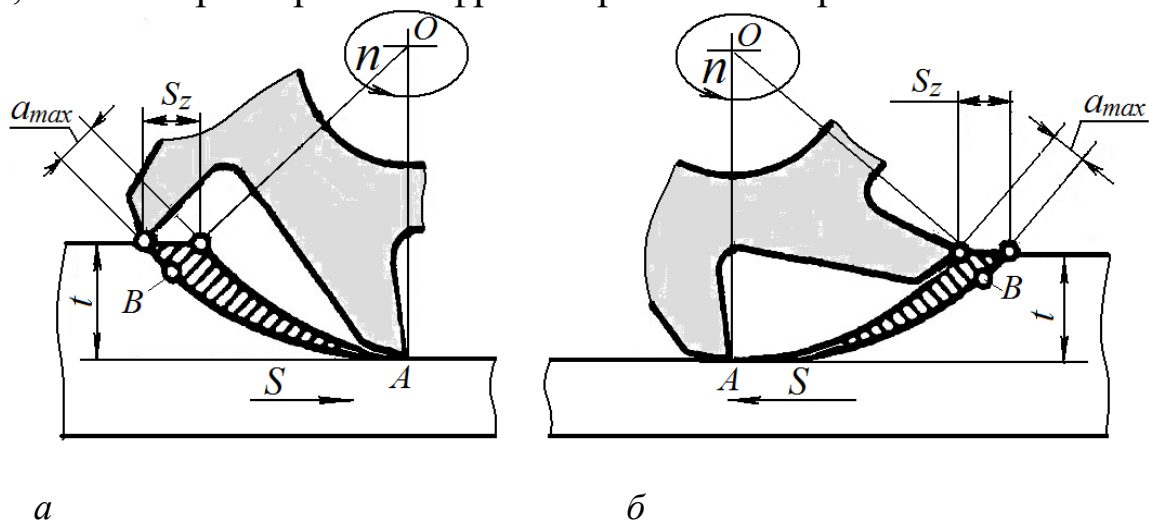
Схемы фрезерования: *a* – попутное; *б* – встречное
